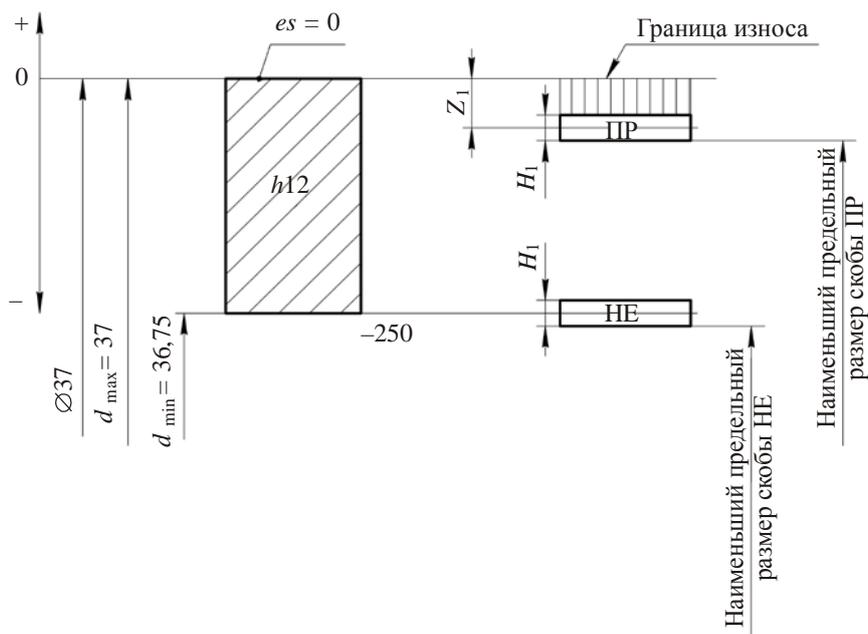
Схема расположения полей допусков рабочих калибров-скоб
